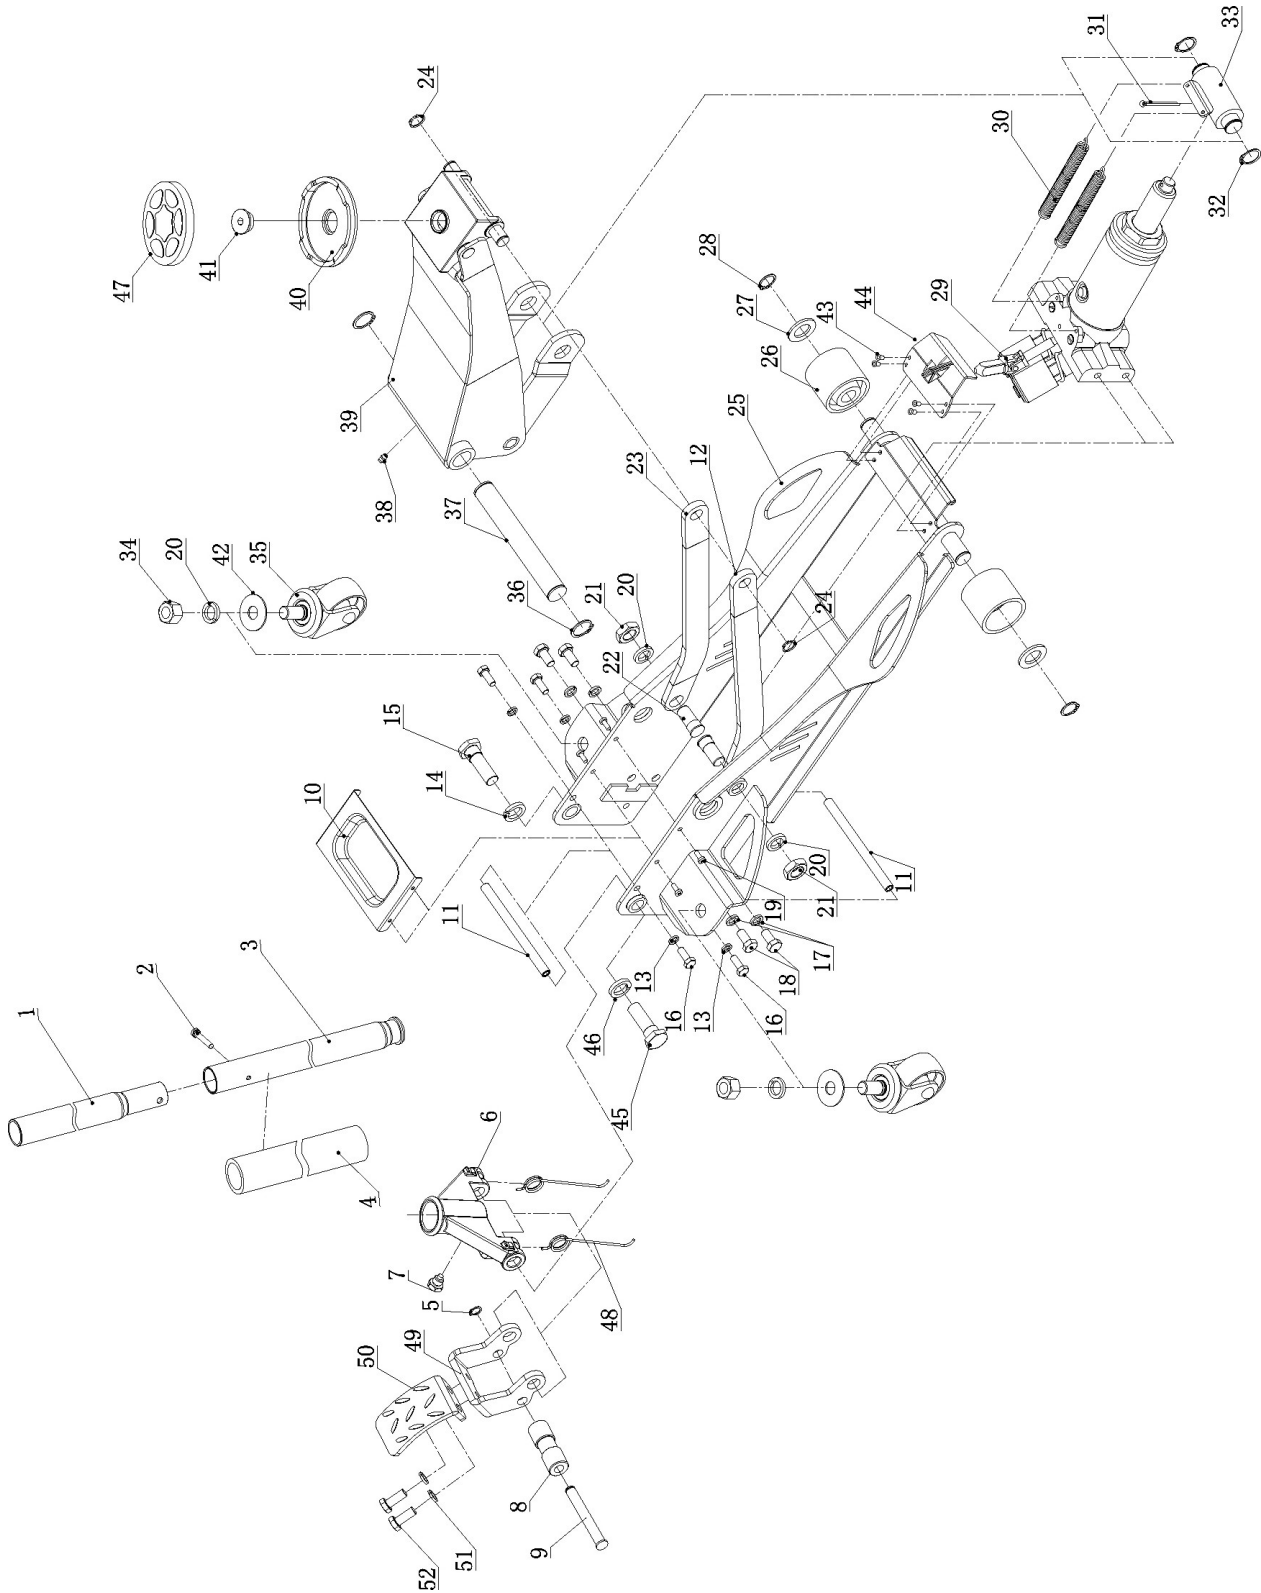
Explosionszeichnung SRWH 2500 LFH
